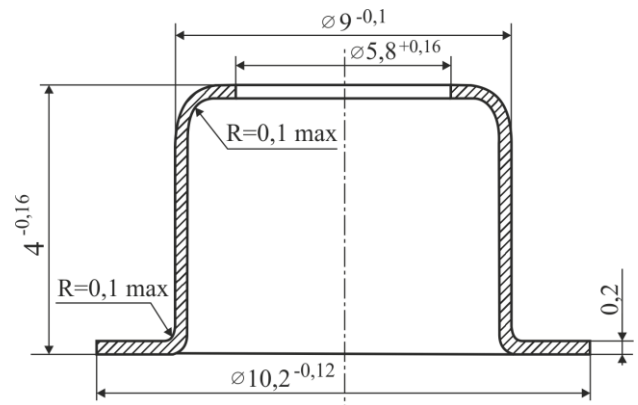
Габаритні розміри кришки корпусу ФД
